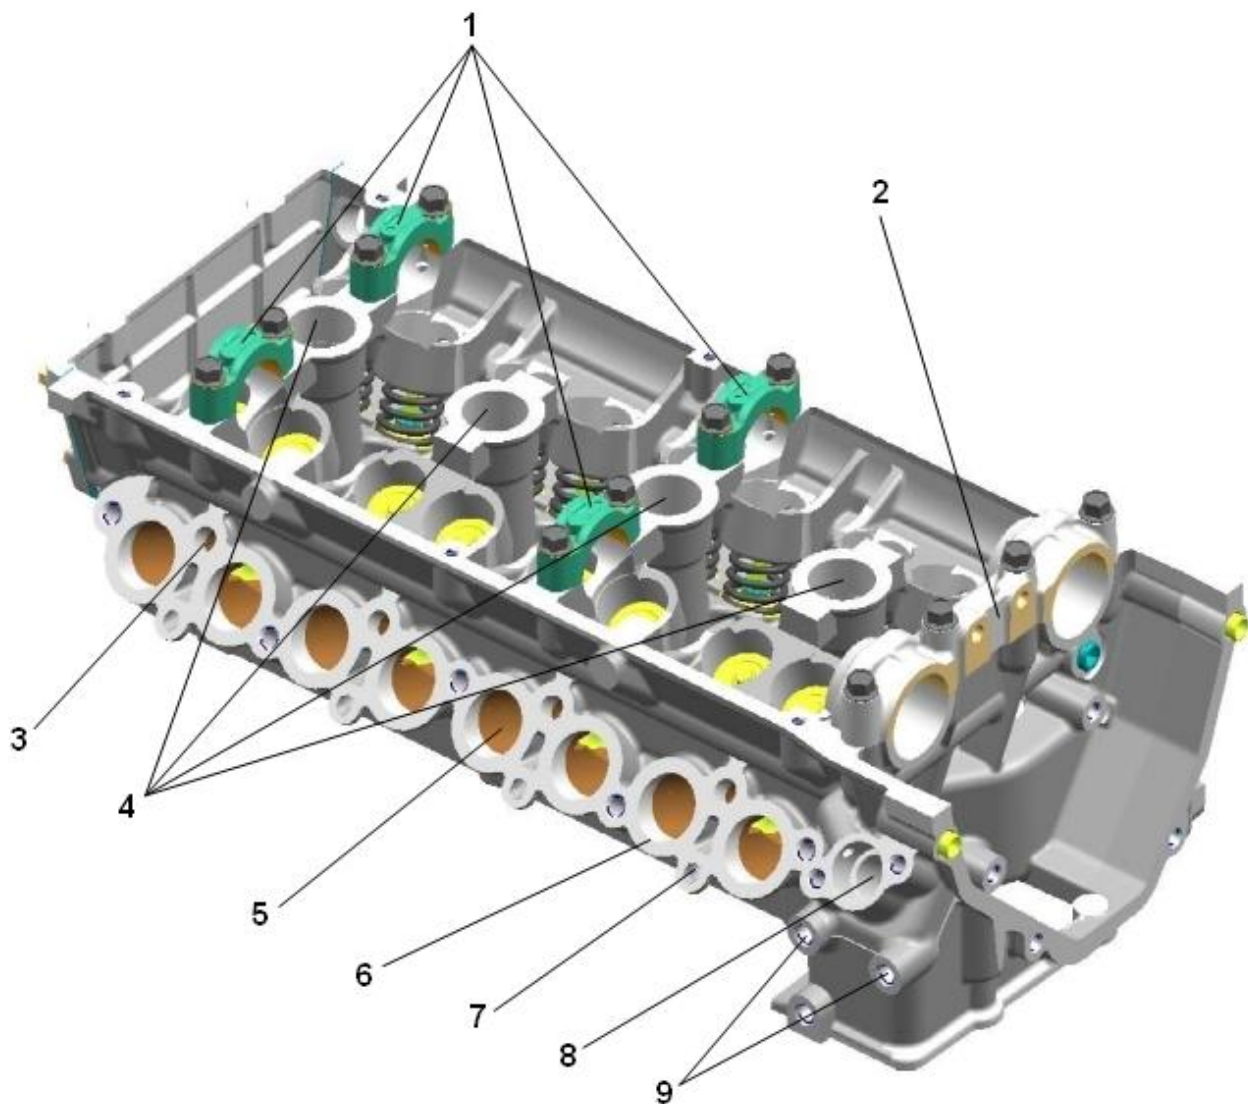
Головка цилиндров. Вид на фланец впускной трубы, верхнюю плоскость и фланец крепления передней крышки:
